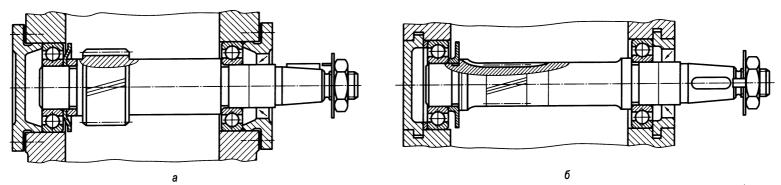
Вал-шестерня цилиндрического зубчатого редуктора (а – исполнение со свободным входом зубонарезного инструмента; б – врезная шестерня)
